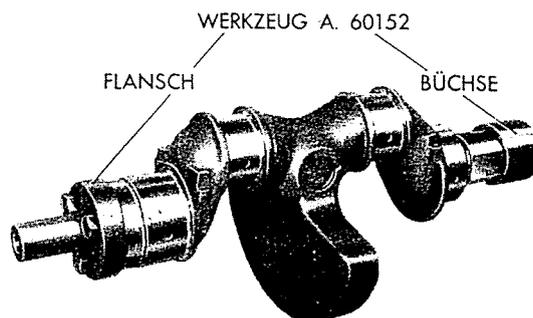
Kurbelwelle und Aufspannwerkzeug zum Nachschleifen.
